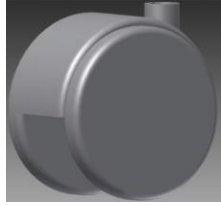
Колесо опори для ходьби, конструкція якого виявилась невдалою
